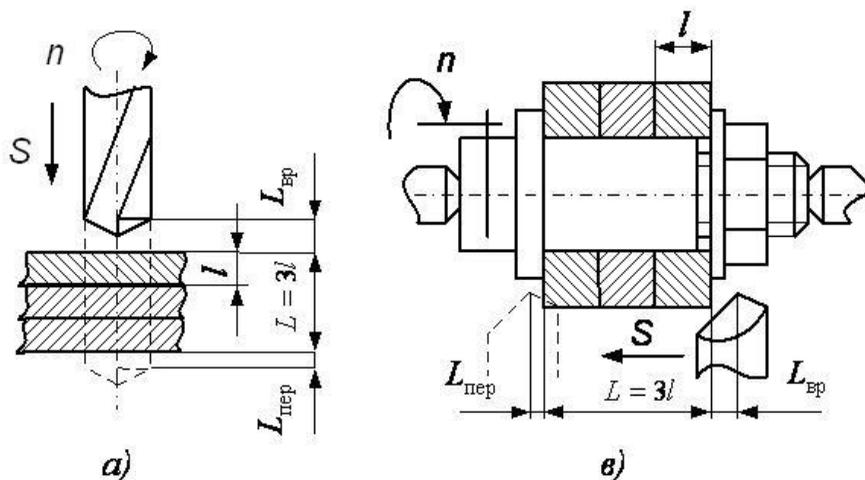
Схемы одноинструментной обработки деталей пакетами
